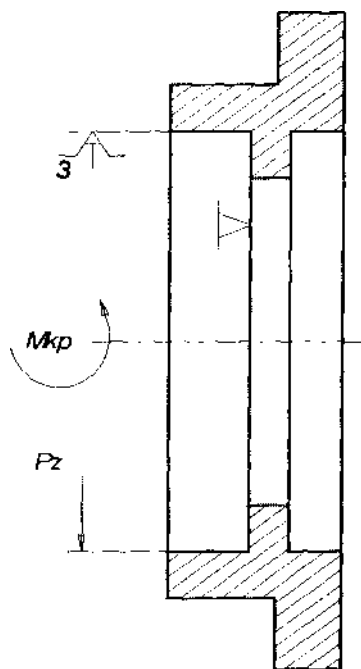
Схема закріплення заготовки в пристрої
